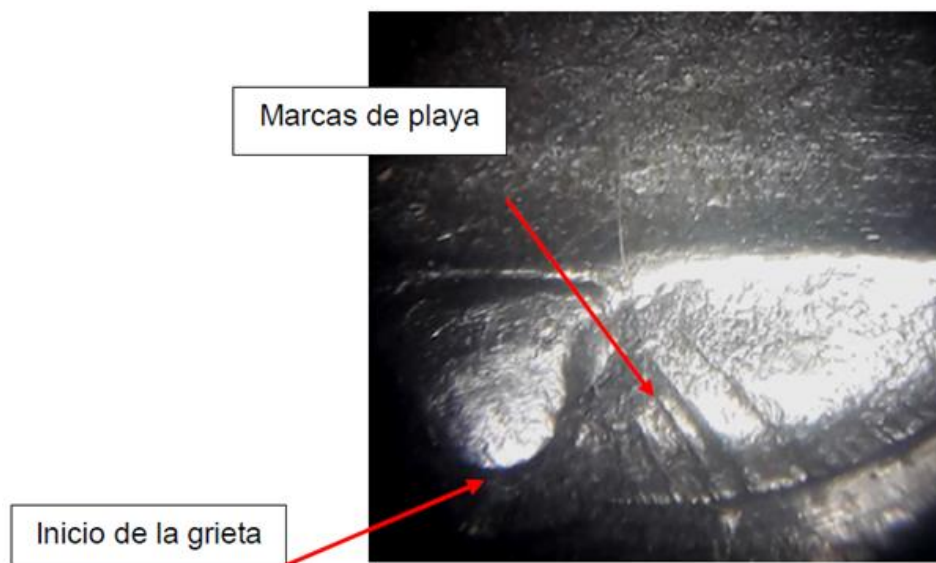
Inspección visual de la superficie de fractura del tornillo M16, se observa que la grieta se inicia en el filete de la rosca, se observan también marcas de playa al inicio de la grieta [26].
